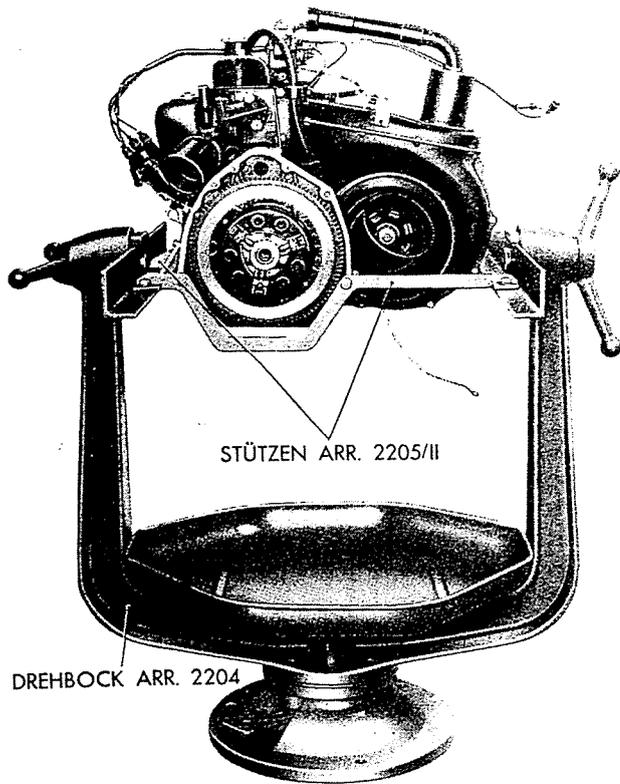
Der mit den Stützen Arr. 2205/II am Drehbock Arr. 2204 befestigte Motor.
